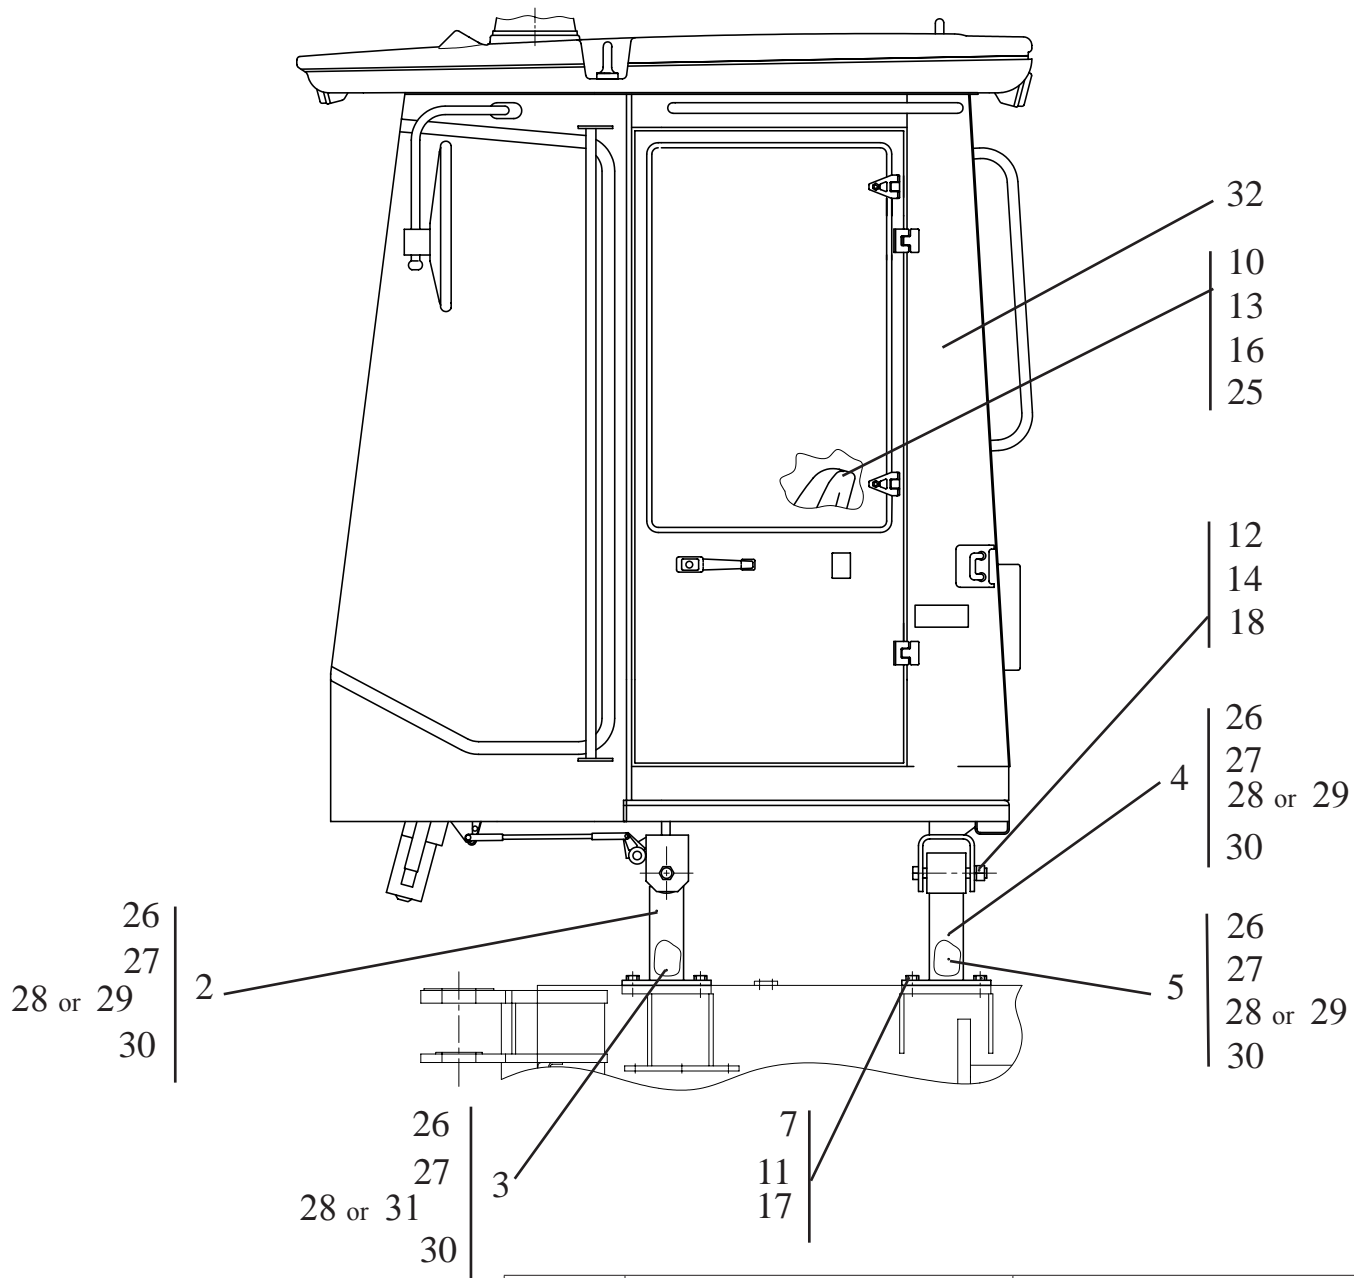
ТО-18Б.85.00.000-06	Установка кабины
